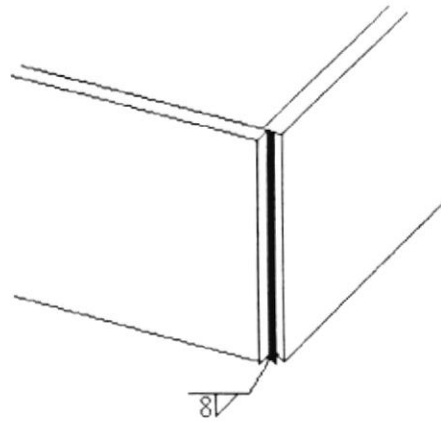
Dibujo del cordón de soldadura
